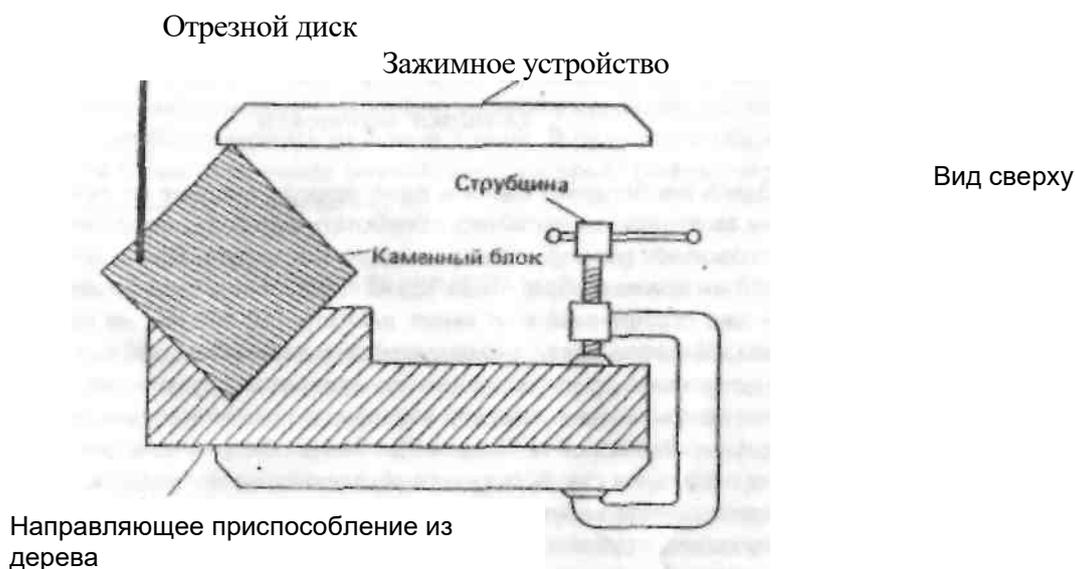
Деревянный кондуктор для отпиливания заготовок шаров.
